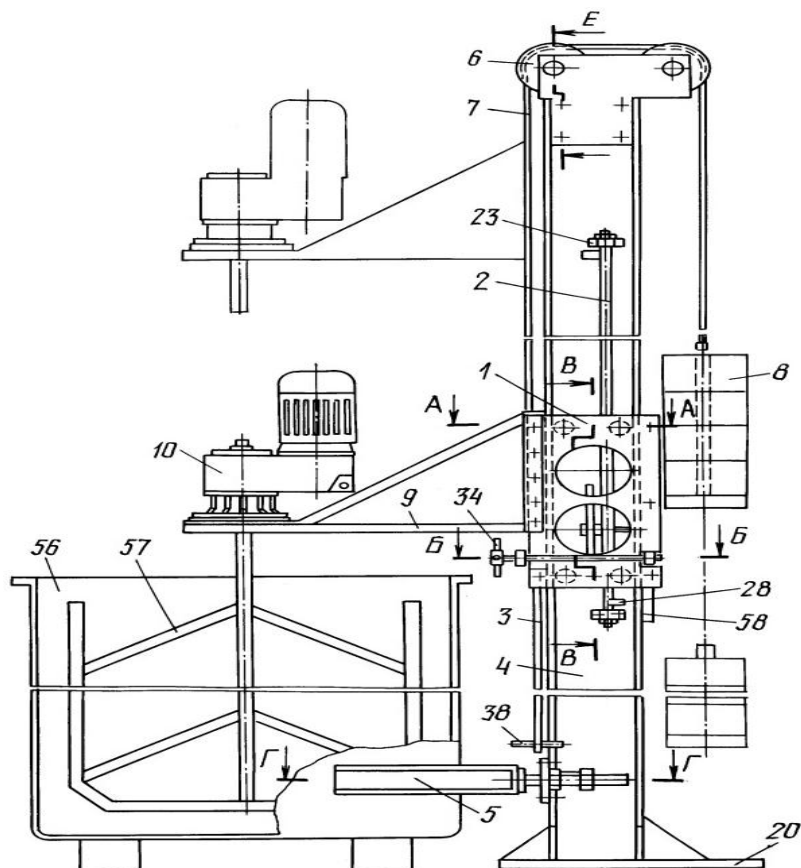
Общий вид устройства для размешивания краски вид сбоку
